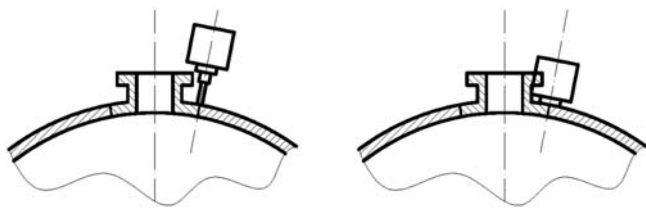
Ограничения по размеру головок для фрикционной сварки
